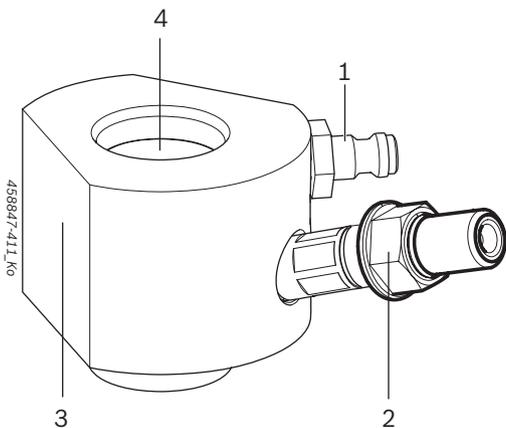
Испытательный адаптер с патрубками напорной трубы
